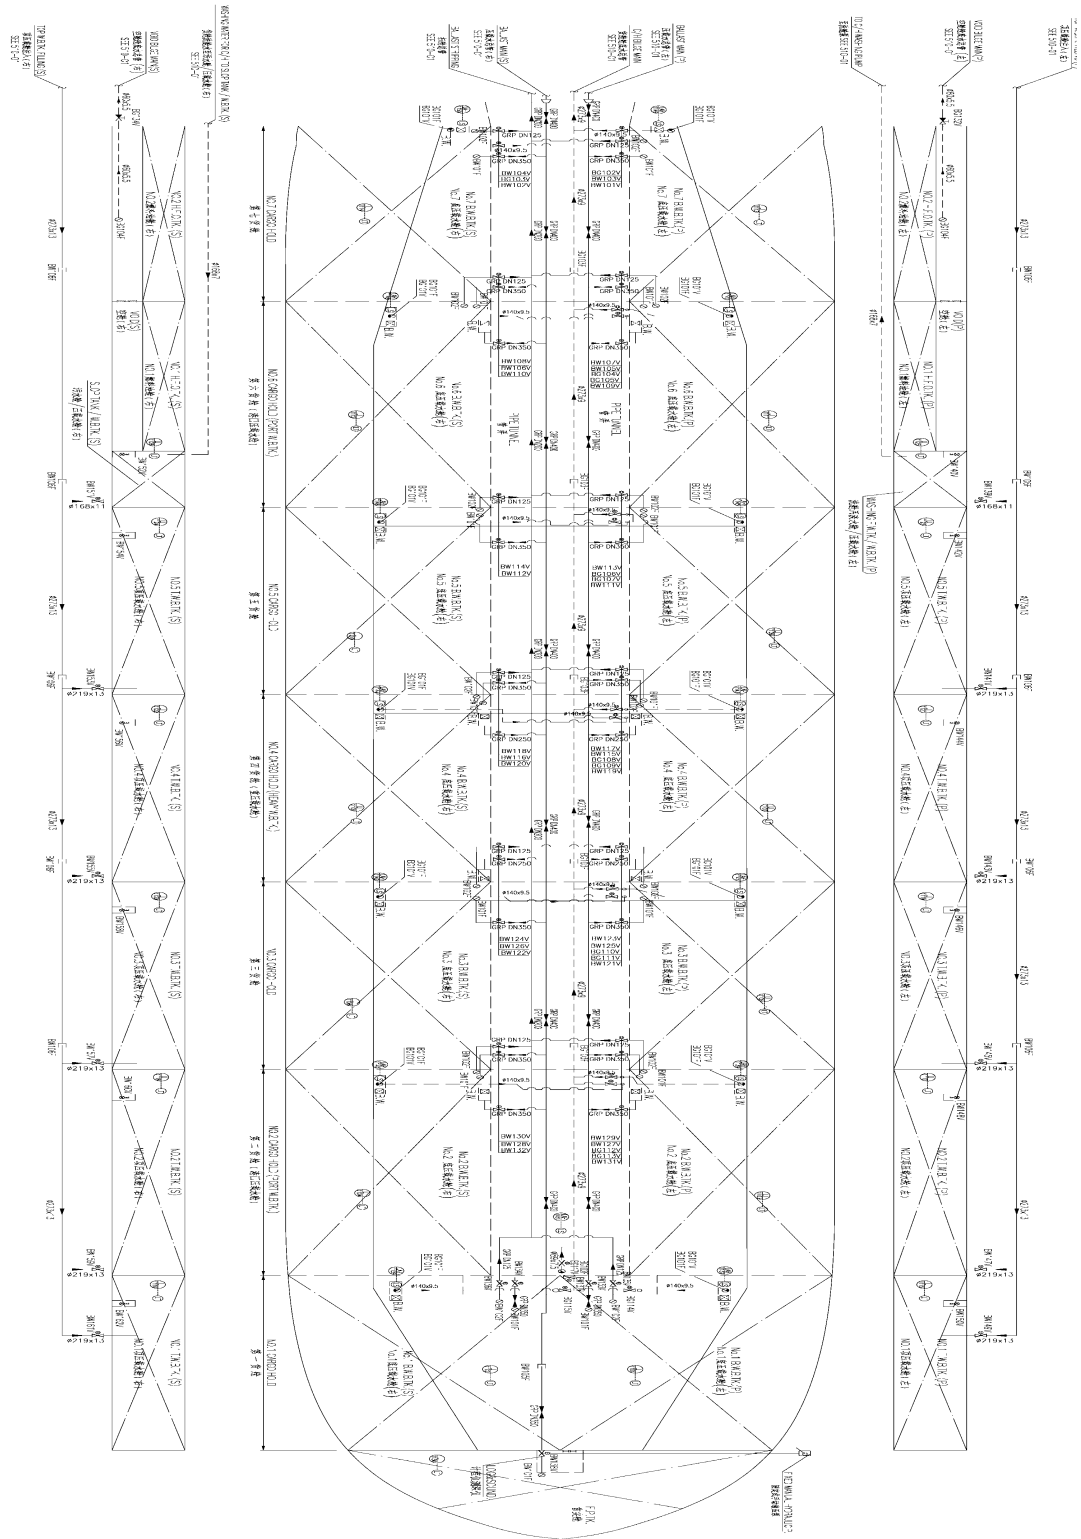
Σχέδιο Γενικής Διάταξης (General Arrangement Plan)
